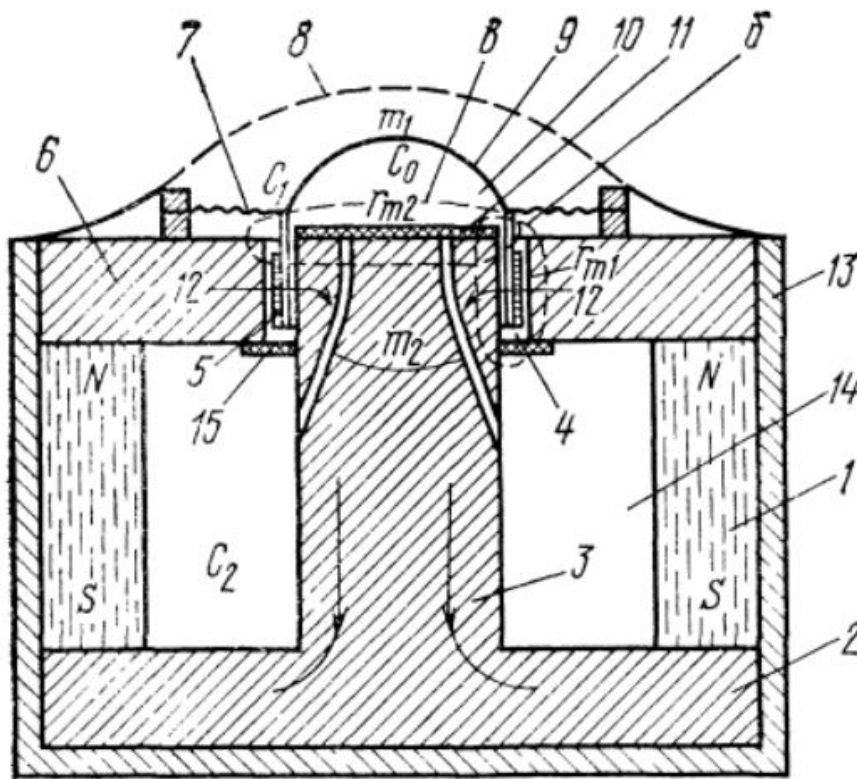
Конструкція динамічного мікрофону-приймача
